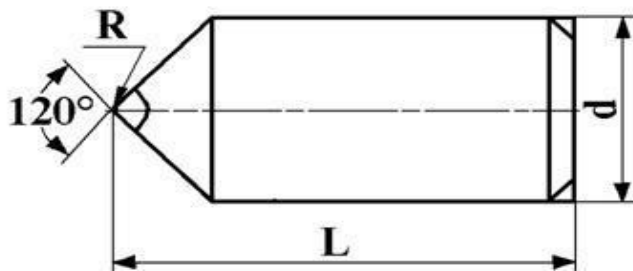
Алмазний інструмент для вигладжування поверхонь деталі
